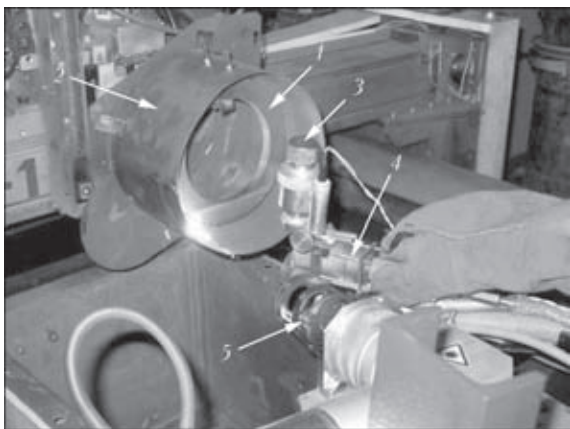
Стенд для поверхностного лазерно-микроплазменного легирования: 1 – образец, закрепленный в захватах; 2 – защитный кожух; 3 – дозатор порошка; 4 – микроплазматрон; 5 – лазерная фокусирующая головка
